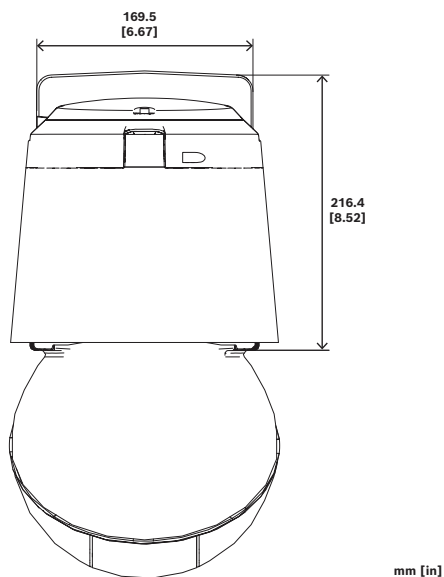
Dimensions en mm de la caméra sur NDA-7100-PEN | NDA-7100-PENF (vue avant)
